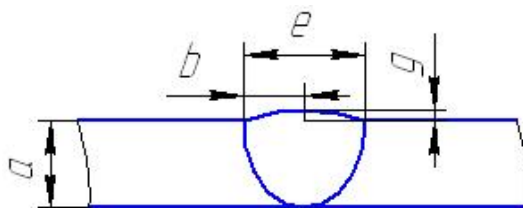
Форма проварювання при зварюванні в середовищі захисних газів
